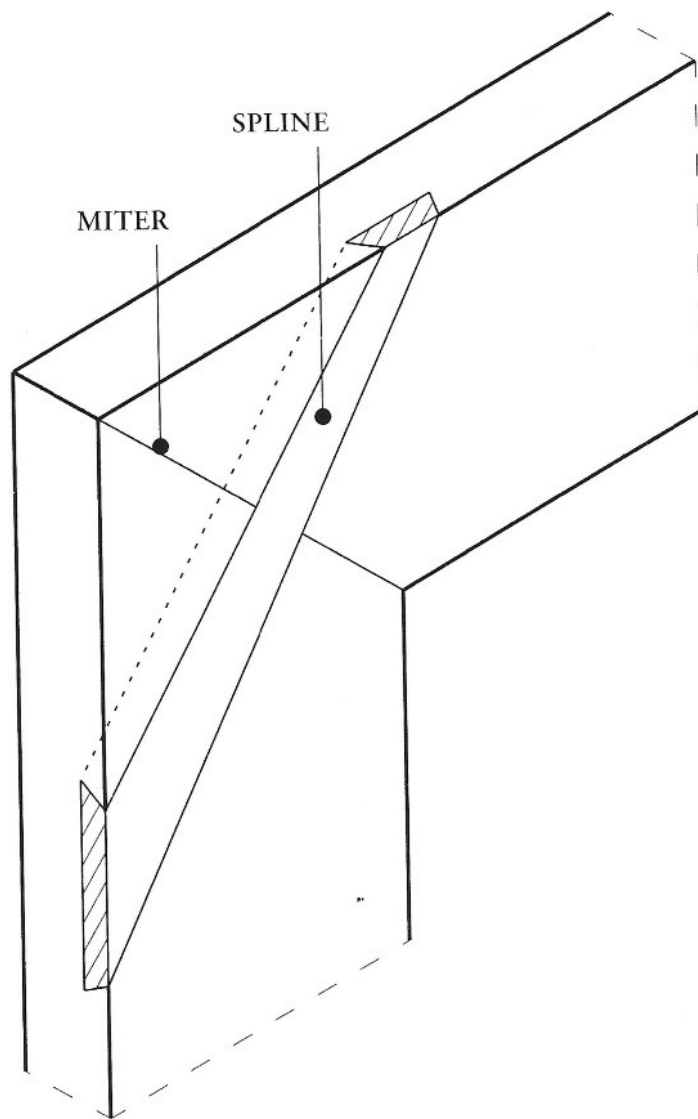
38 Holandský typ boltcového rámu, Utrecht 1654.
